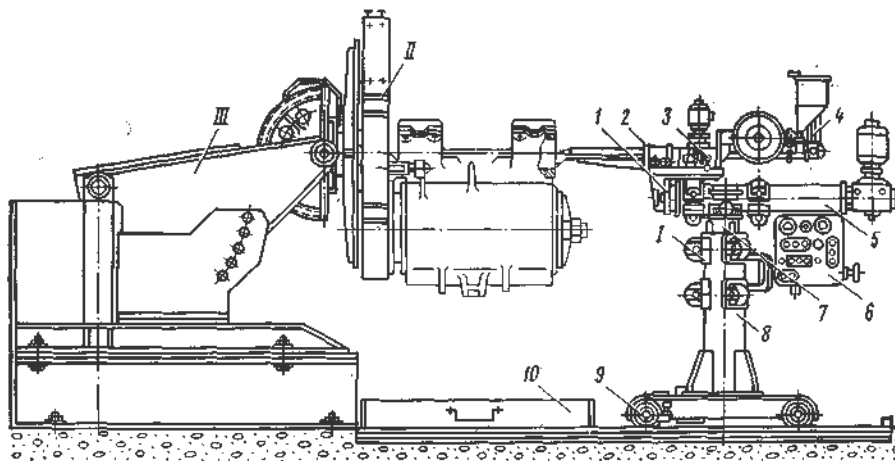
Установка полуавтоматической наплавки горловин остова тягового двигателя
